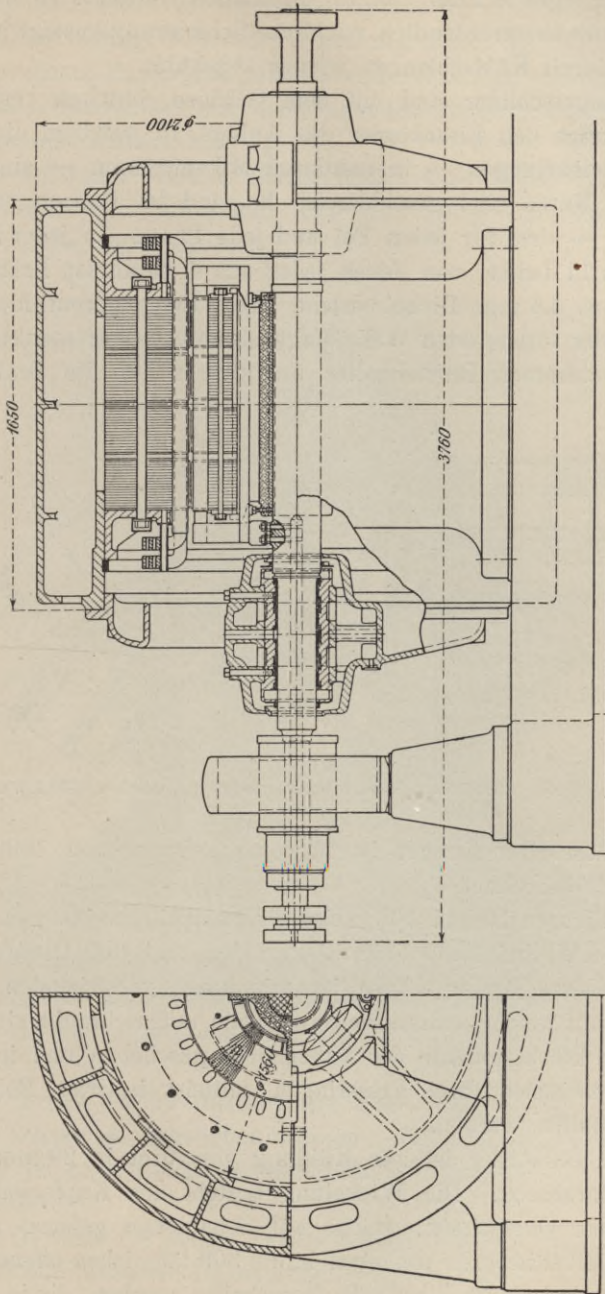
/106. Turbo-Generator mit umlaufendem Magnetfeld von 1200 KW.
